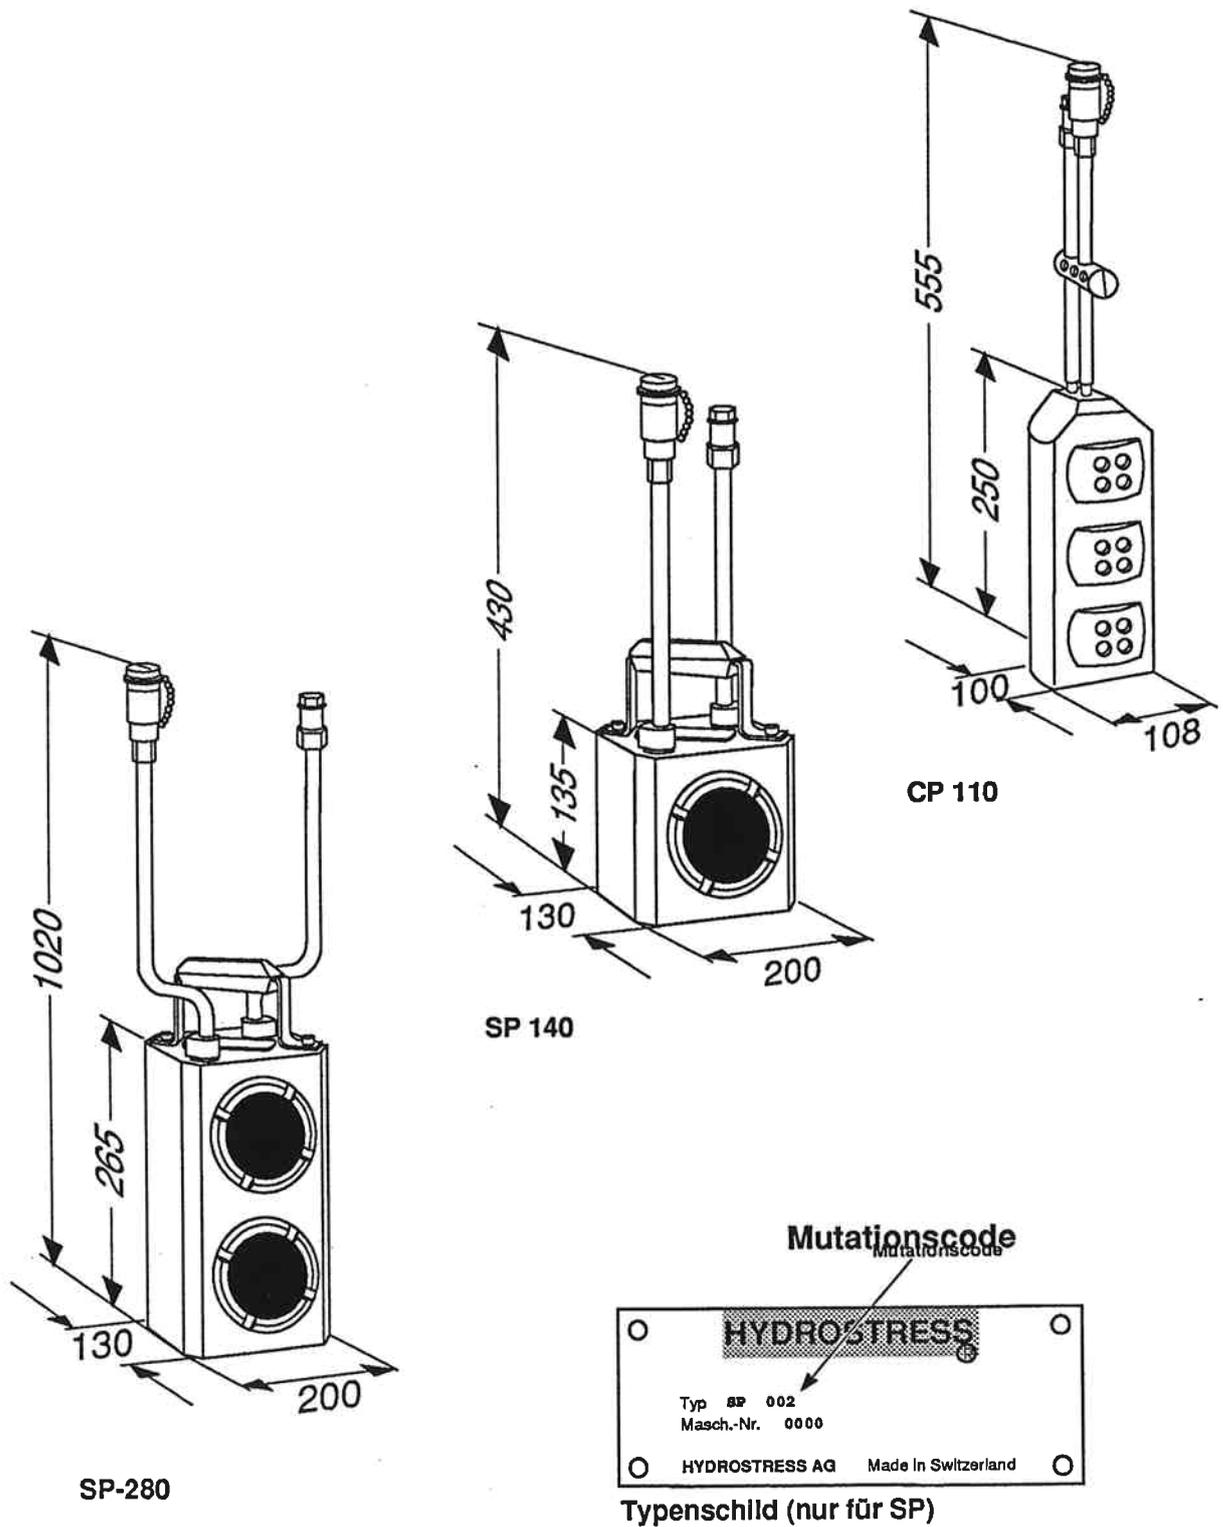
Abmessungen und Typenschild Preßwerkzeuge
